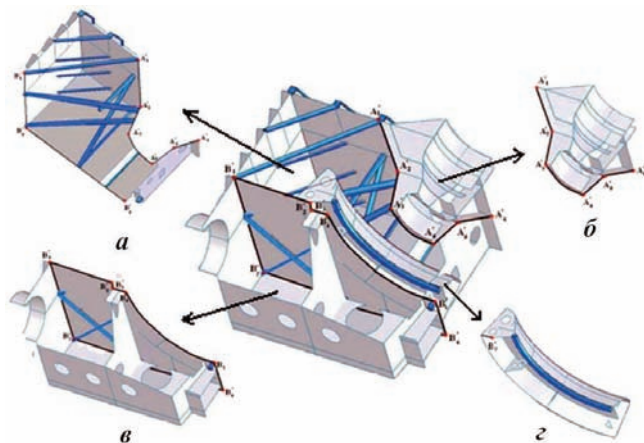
Суперэлементная модель корпуса ЦНД:
